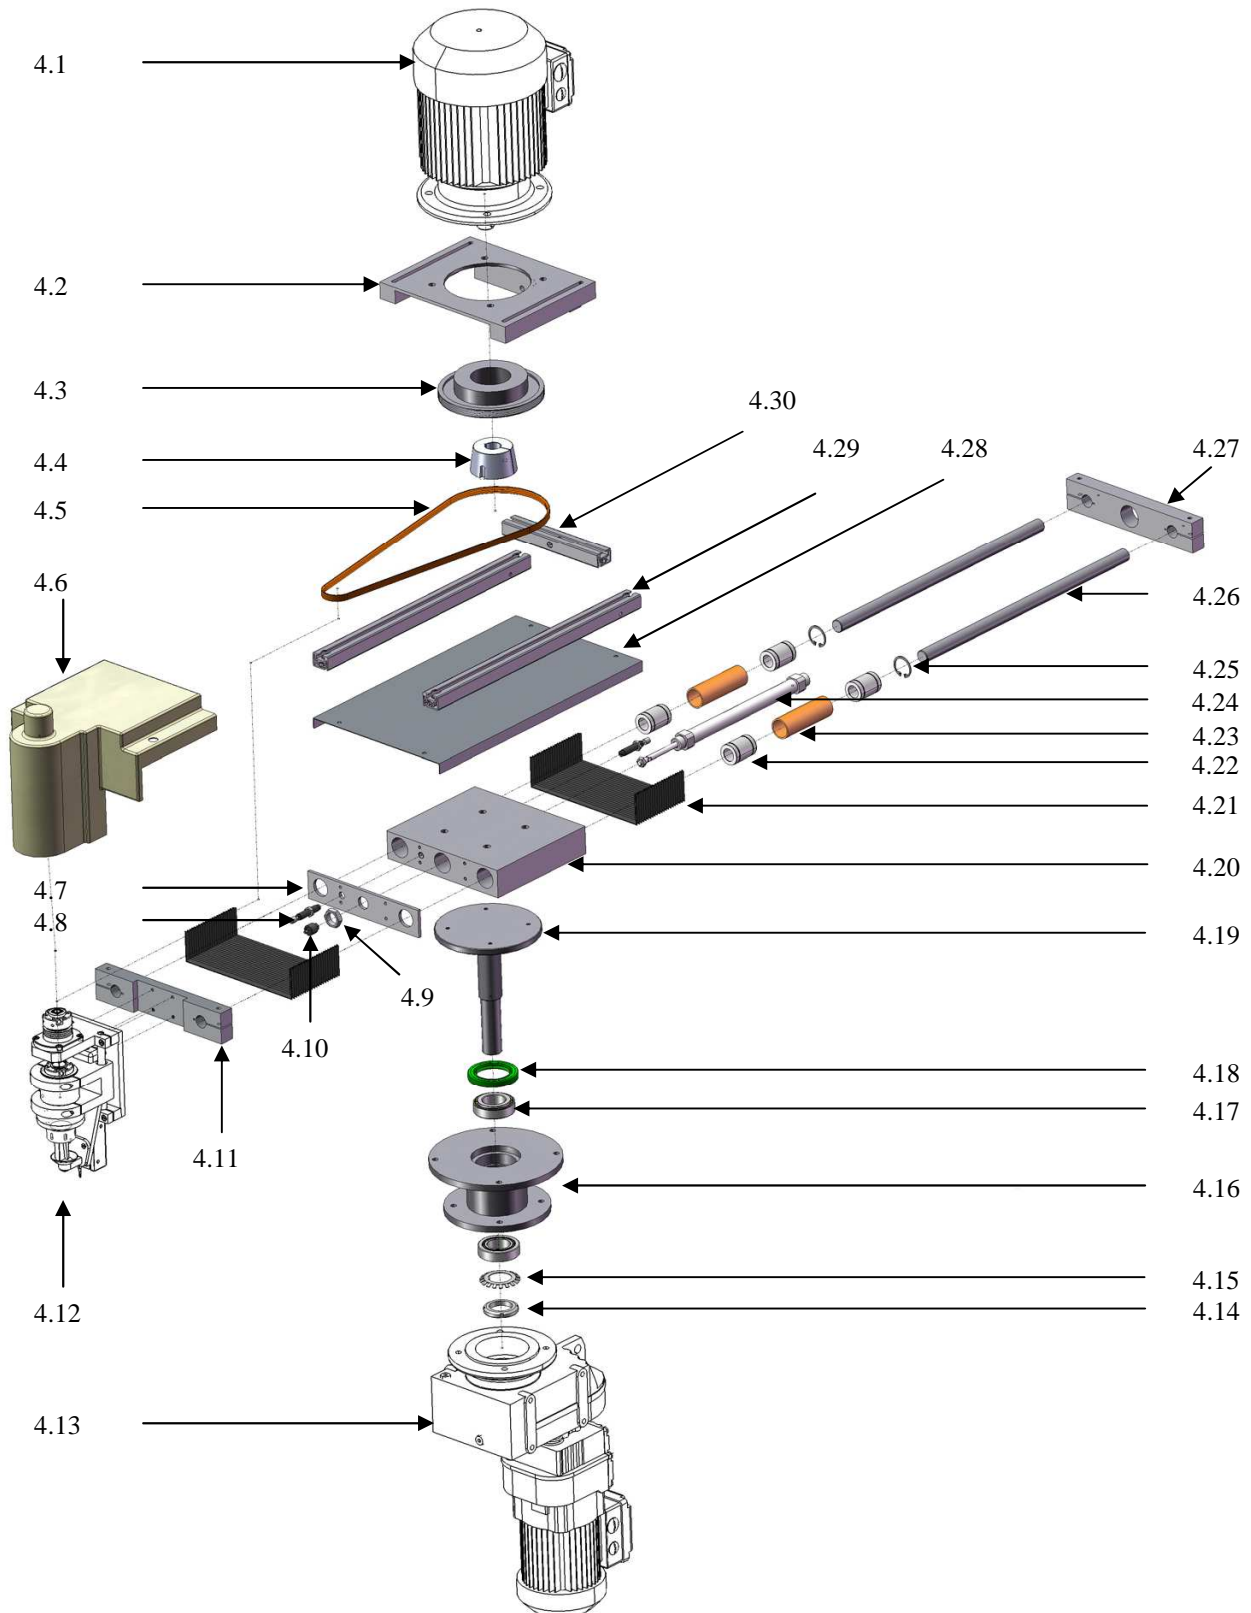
Vista explodida da mesa porta-ferramenta.
